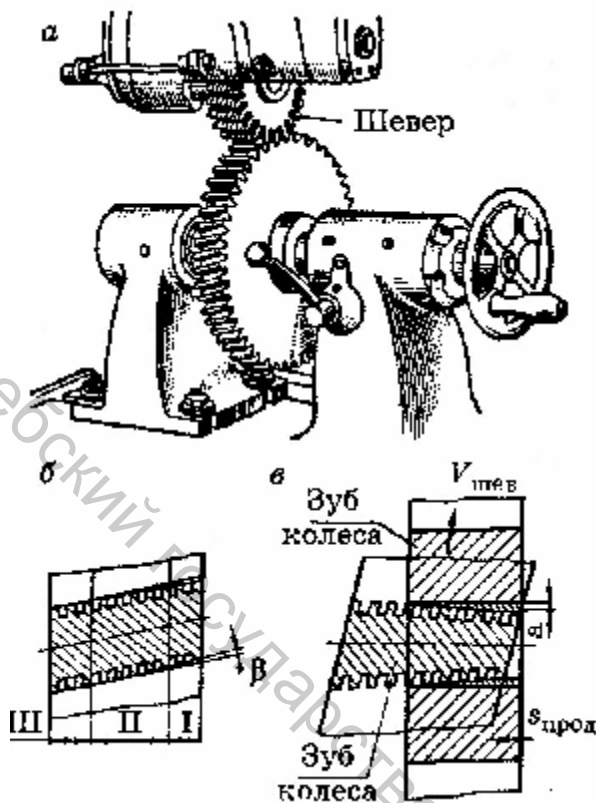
Шевингование цилиндрического зубчатого колеса дисковым шевером: а — общий вид; б и в — схема шевингования за один ход стола
